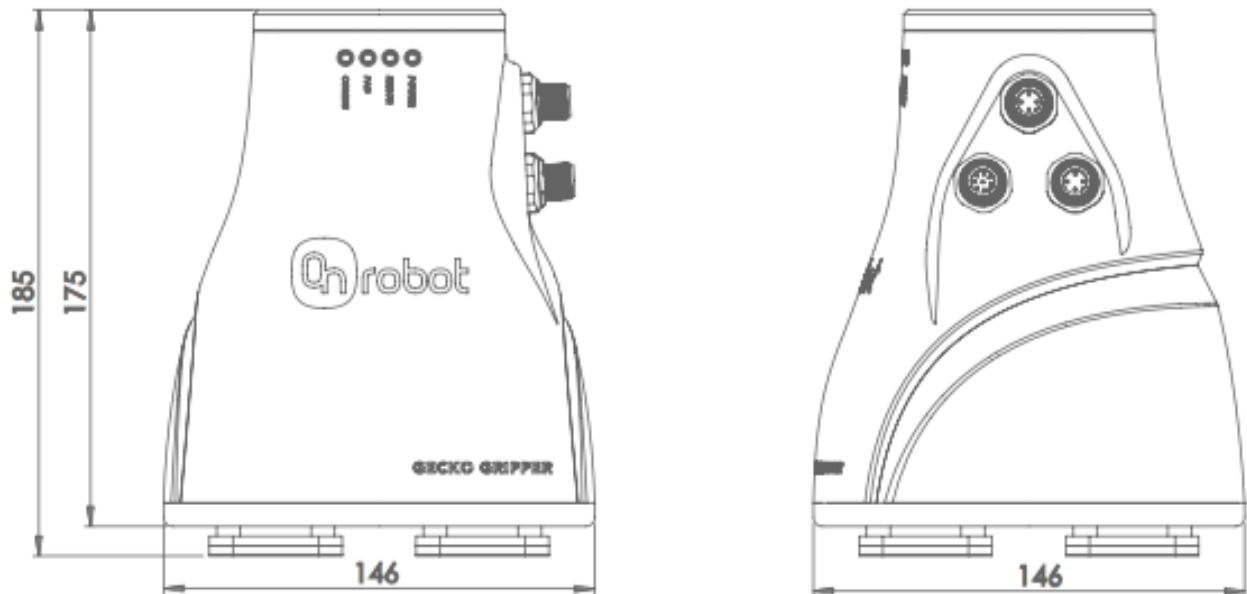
Dimensões frontais e laterais do Gecko Gripper.
